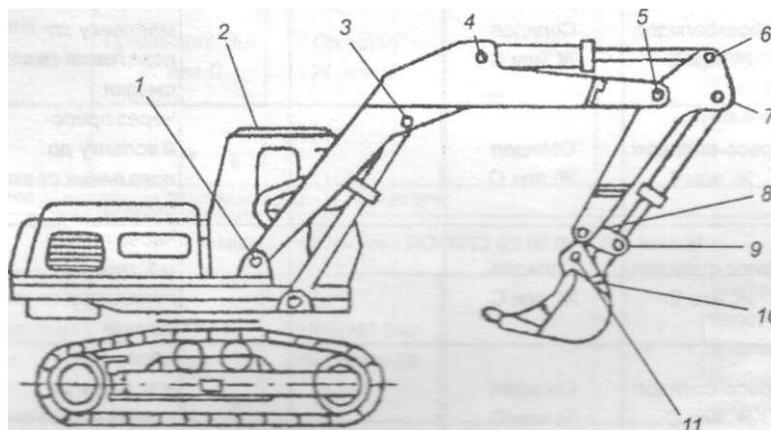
Схема смазки рабочего оборудования обратная лопата.
